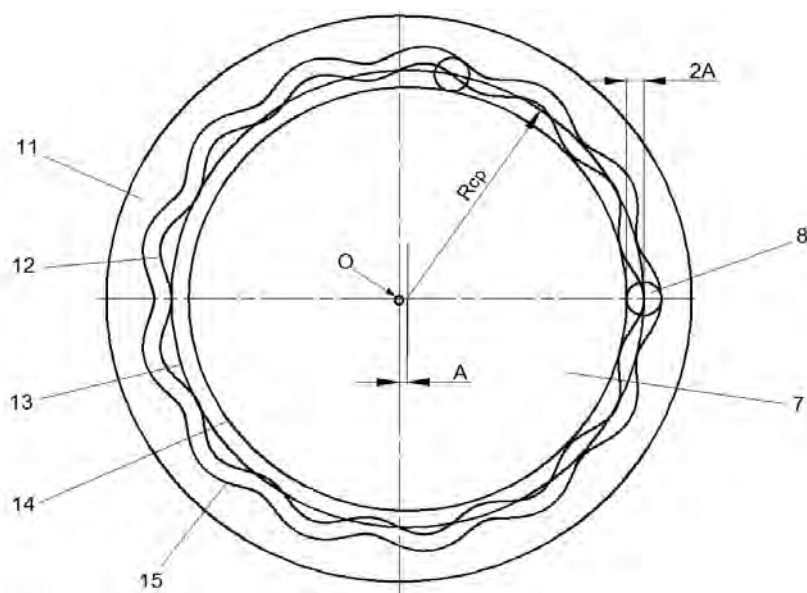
Схема и геометрические параметры деталей зацепления планетарной радиально-плунжерной передачи
